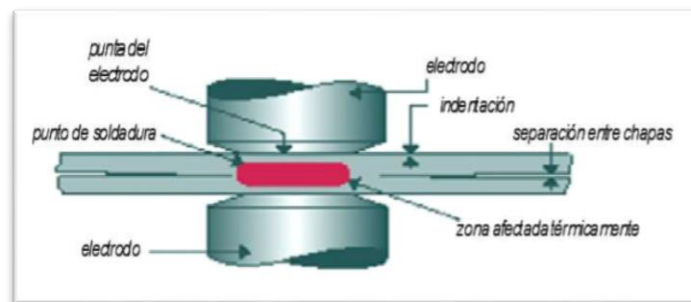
(Esquema de soldadura por puntos)
